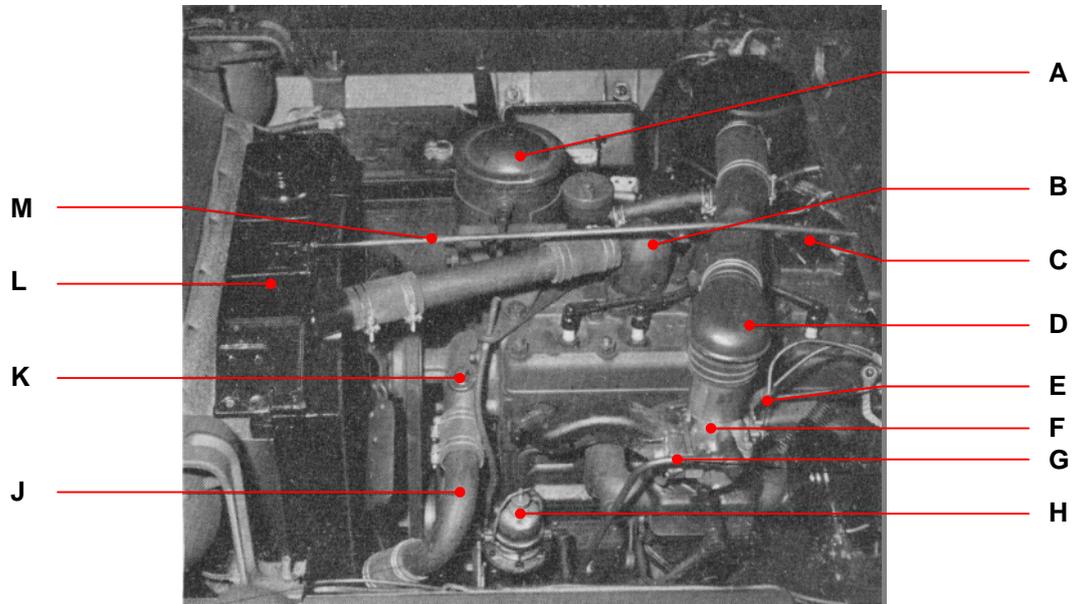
Vue du côté gauche du moteur en place sur le véhicule.
